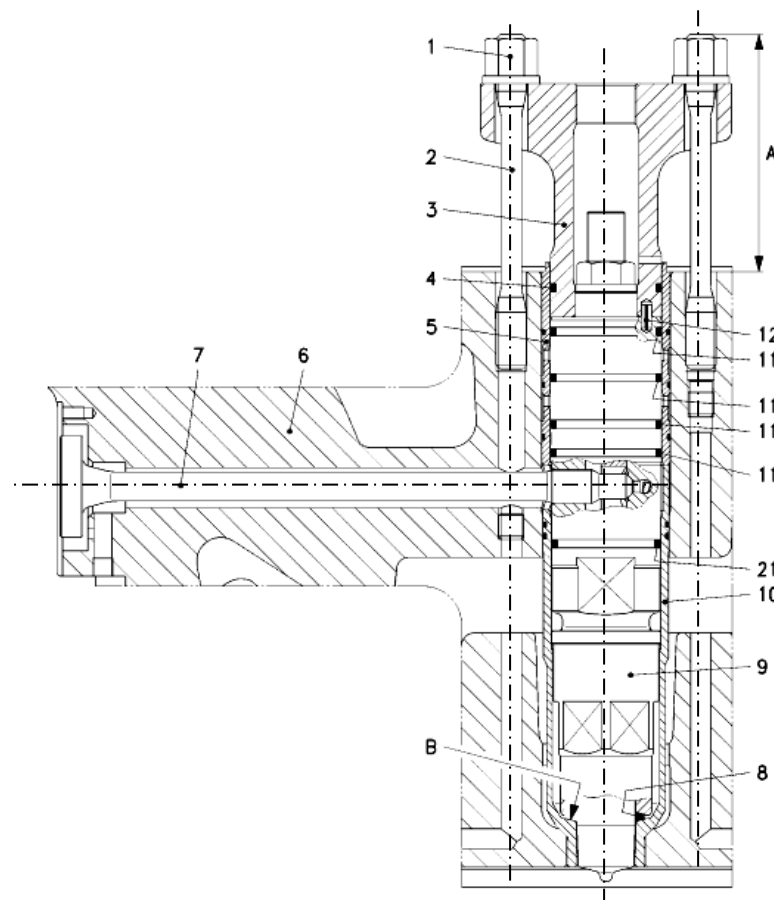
Форсунка з різьбовим з'єднанням: 1 - шестигранна гайка; 2 – стойка; 3 - упорний фланець; 4, 11, 21 - О-подібне кільце ущільнення; 5 – втулка; 6 - головка циліндра; 7 - різьбовий елемент; 8 - ущільнююче кільце; 9 - форсунка; 10 – вставка; 12 – штифт; А – болтова відстань; В – сідло клапана
